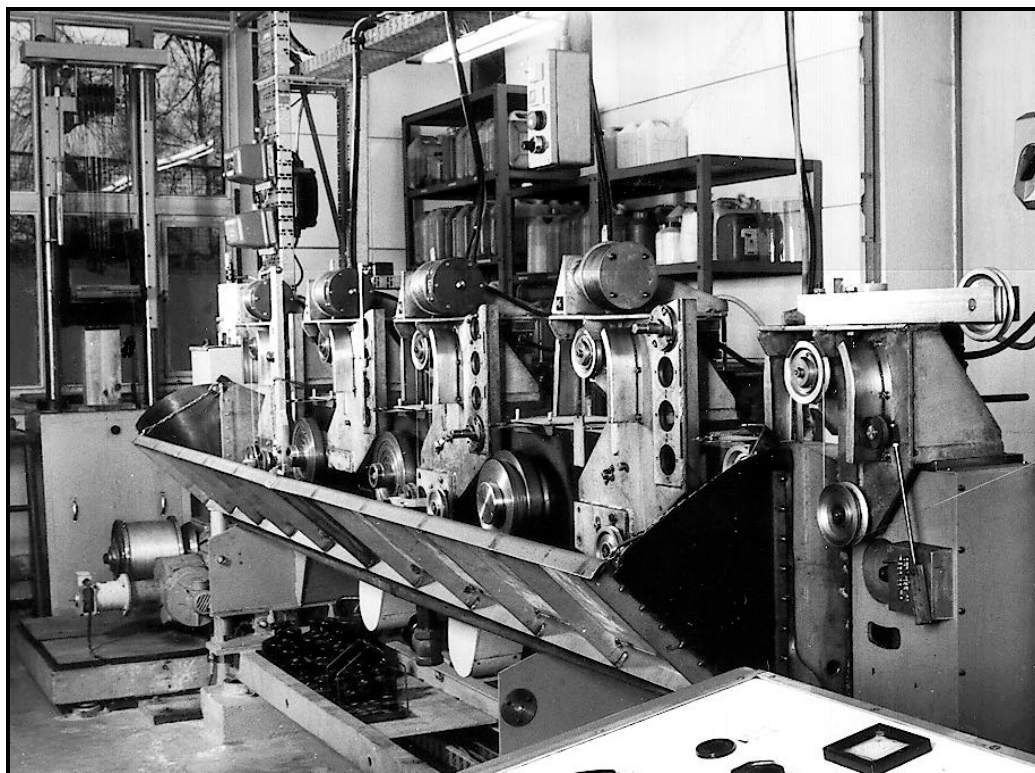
Labor-Feindrahtziehmaschine
